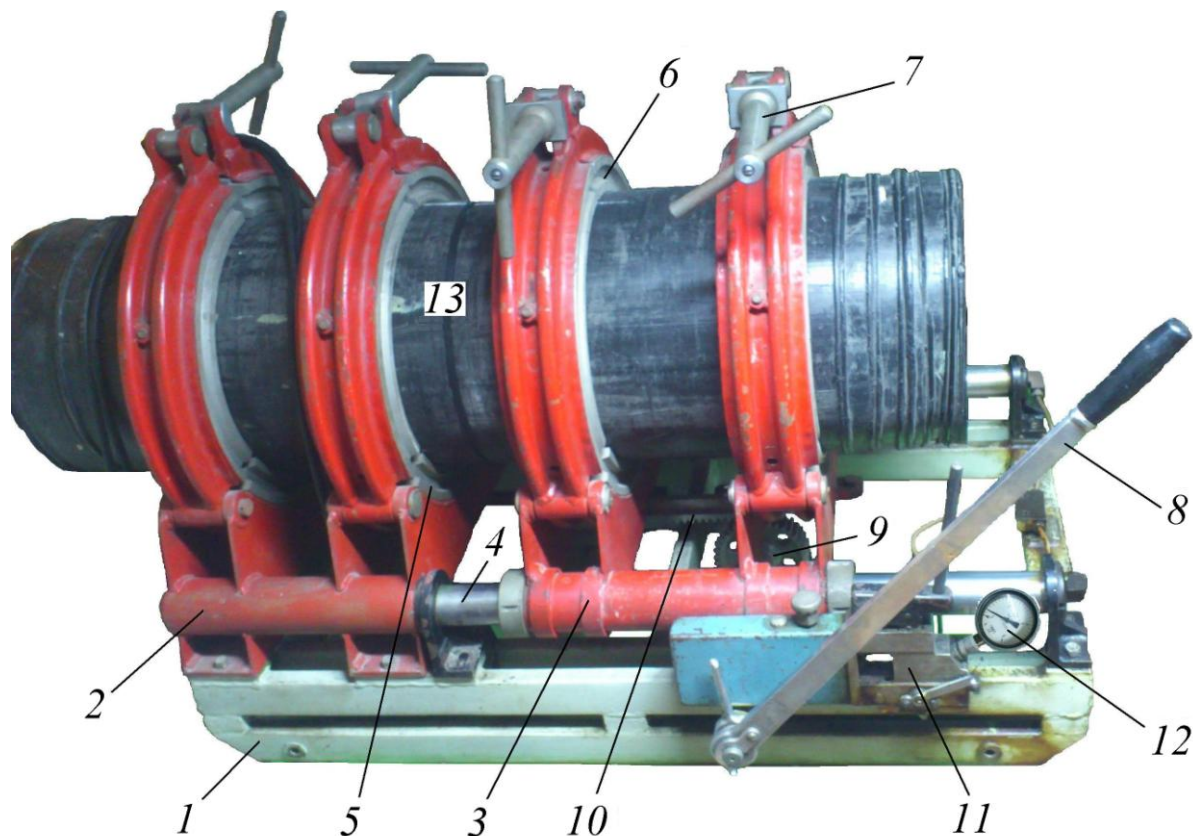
Установка УСРТ-20-40: 1 - рама; 2 – каретка неподвижная; 3 – каретка подвижная; 4 – цилиндрическая направляющая; 5 - полуобойма; 6 – сектор; 7 – винт; 8 – рычаг; 9 – зубчатое колесо; 10 – зубчатая рейка; 11 – гидравлический насос; 12 - манометр; 13 – свариваемые трубы
